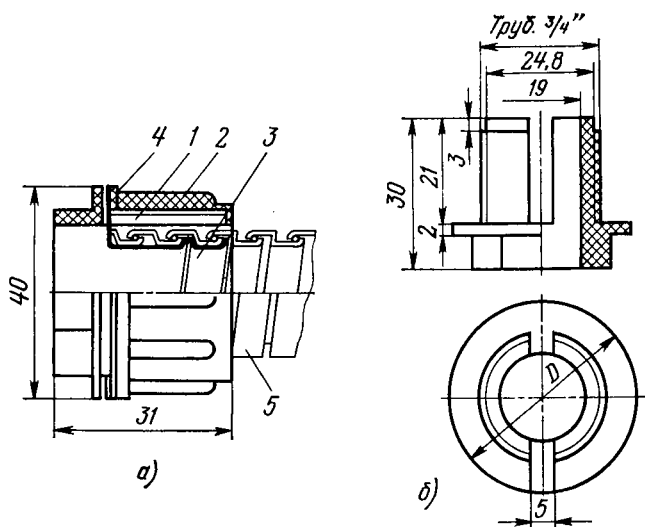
Соединитель короба с металлорукавом, $D_y=15$ мм.
